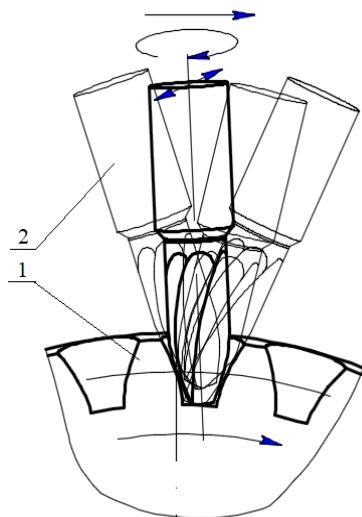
Рух накатника та пальцевої фрези під час виготовлення зубозаокруглюючої впадини
